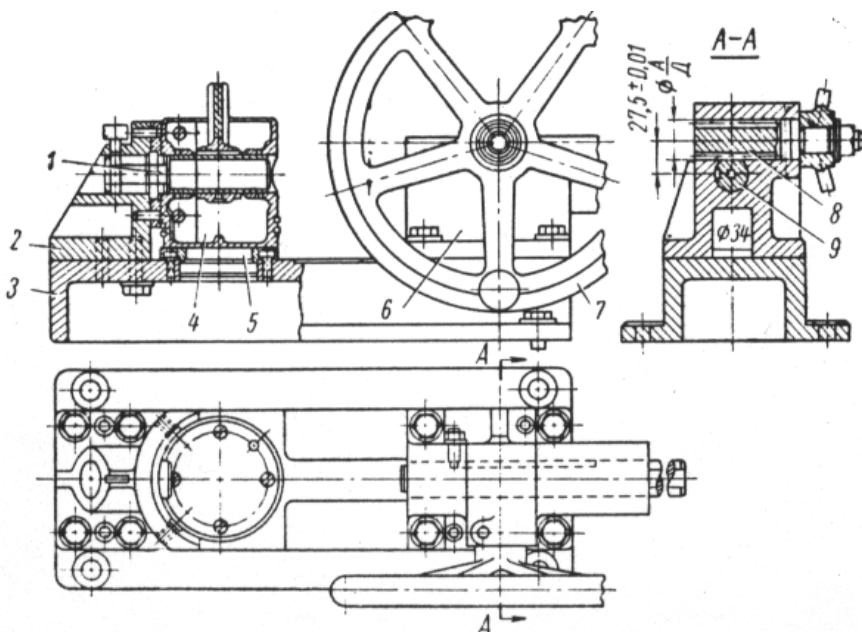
Приспособление для запрессовки и выпрессовки поршневого пальца: 1 – упор; 2 – кронштейн; 3 – корпус; 4 – поршень; 5 – подставка поршня; 6 – бабка; 7 – маховичок; 8 – шестерня; 9 – шток-рейка
